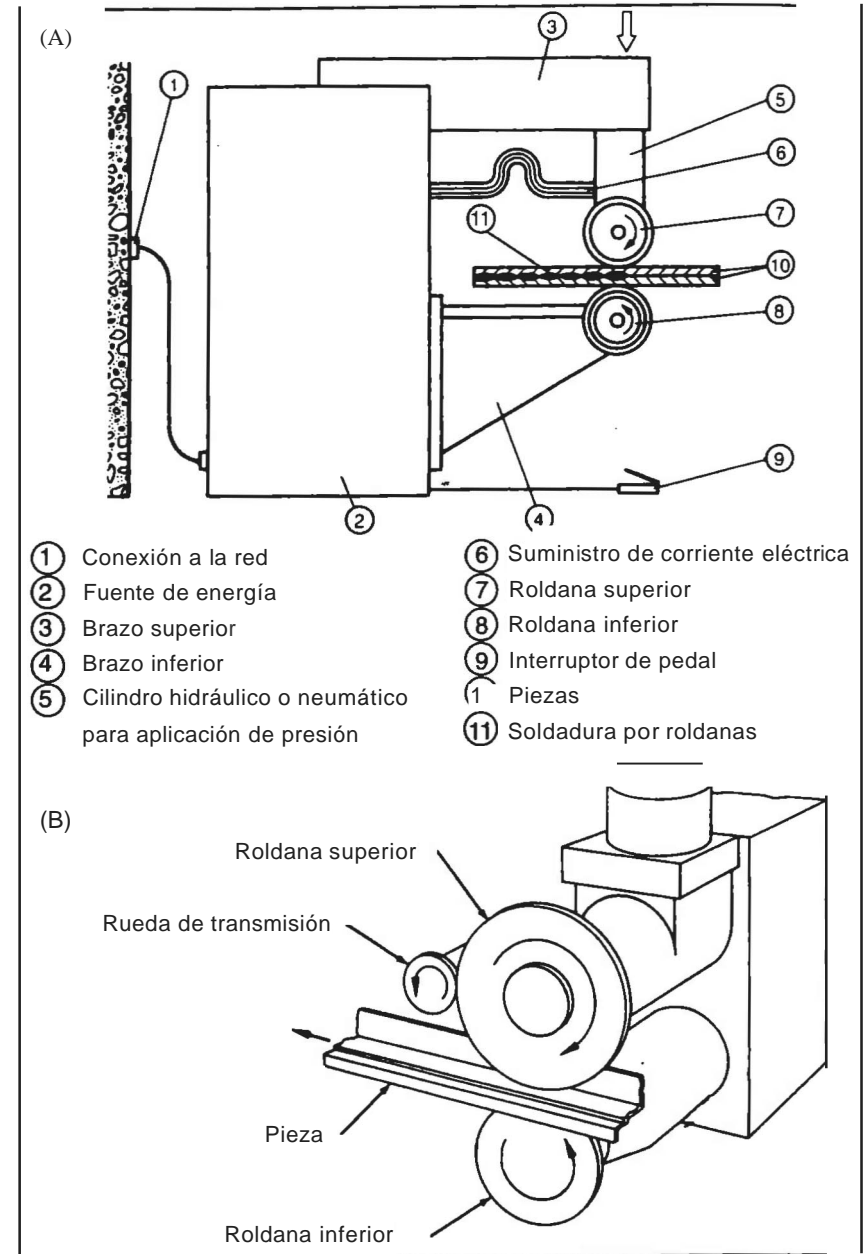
(A) MÁQUINA DE SOLDEO POR ROLDANAS. (B) DETALLE DE LAS ROLDANAS
